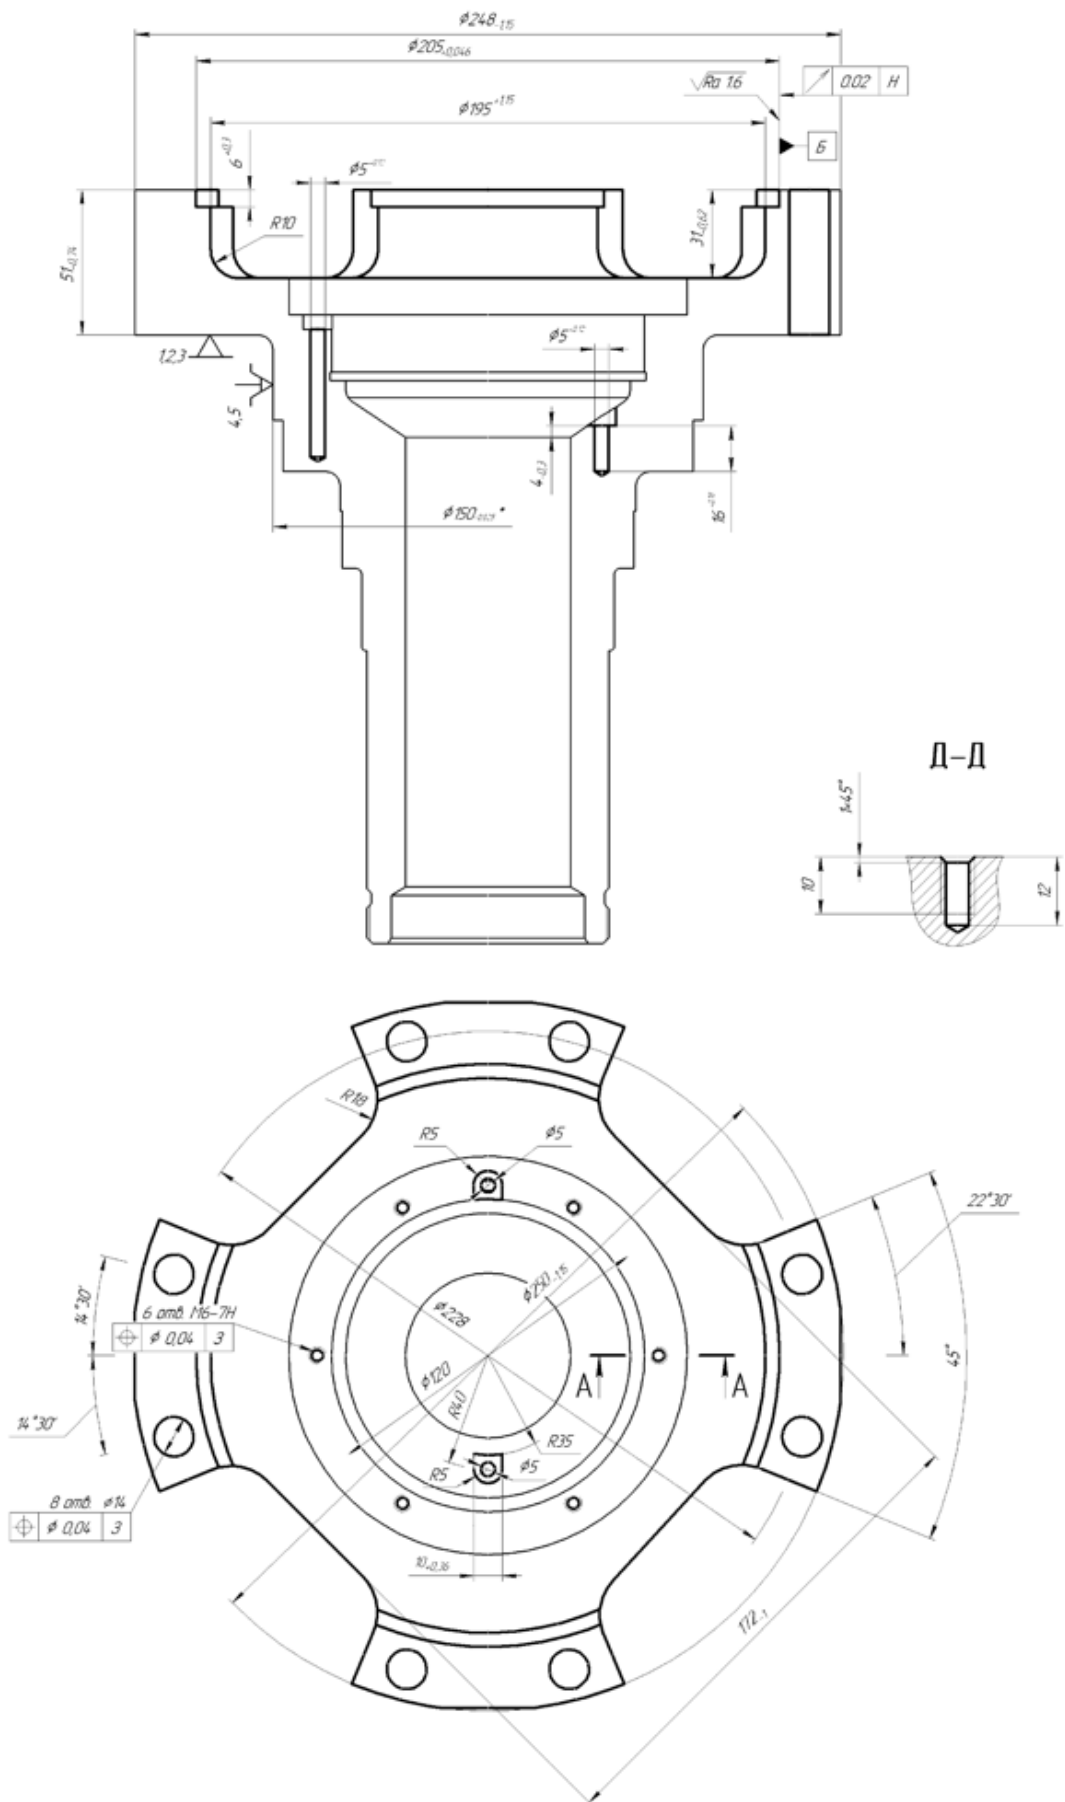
Ескіз обробки до операції 055 Фрезерування з ЧПК
